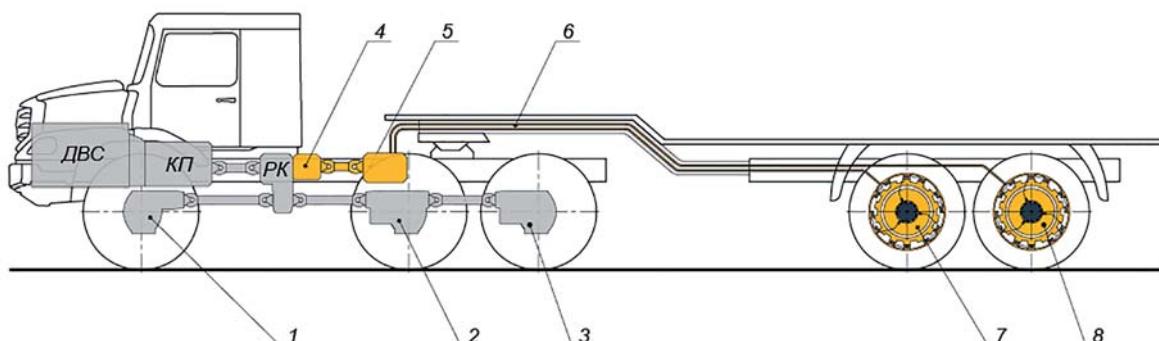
Компоновка агрегатов электрического привода полуприцепа:
